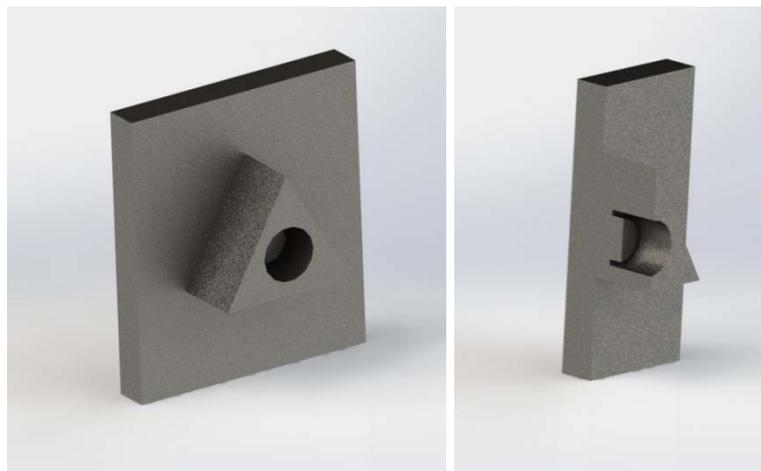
Parte 1 molde cuerpo prisma triangular
